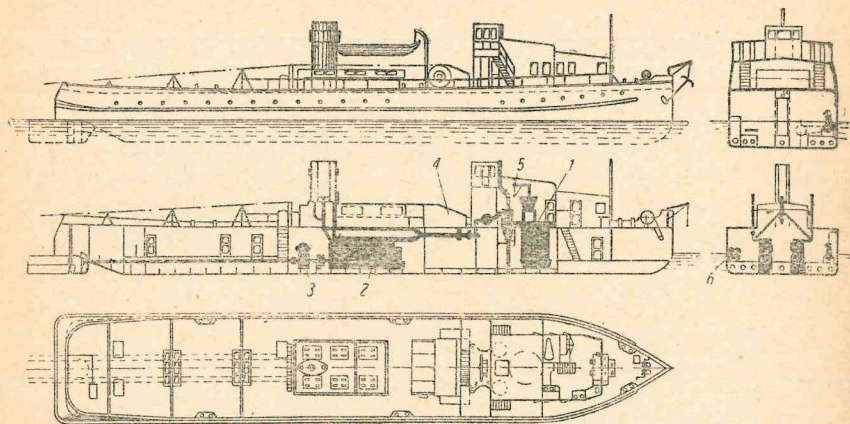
Буксирный газоход „Нарпен I“: 1—газогенератор; 2—моторы; 3—редукторы; 4—вентиляторы; 5—загрузочное устройство; 6—пусковые баллоны сжатого воздуха
